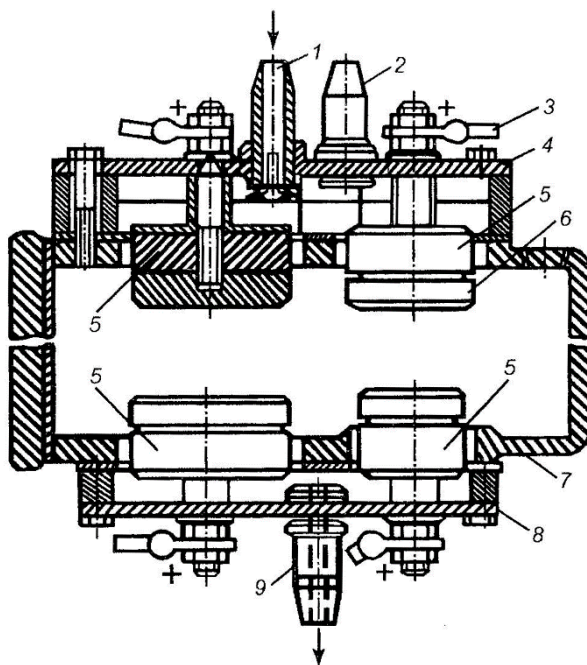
Схема устройства для проточного осталивания отверстий в корпусной детали [1; 14]:
